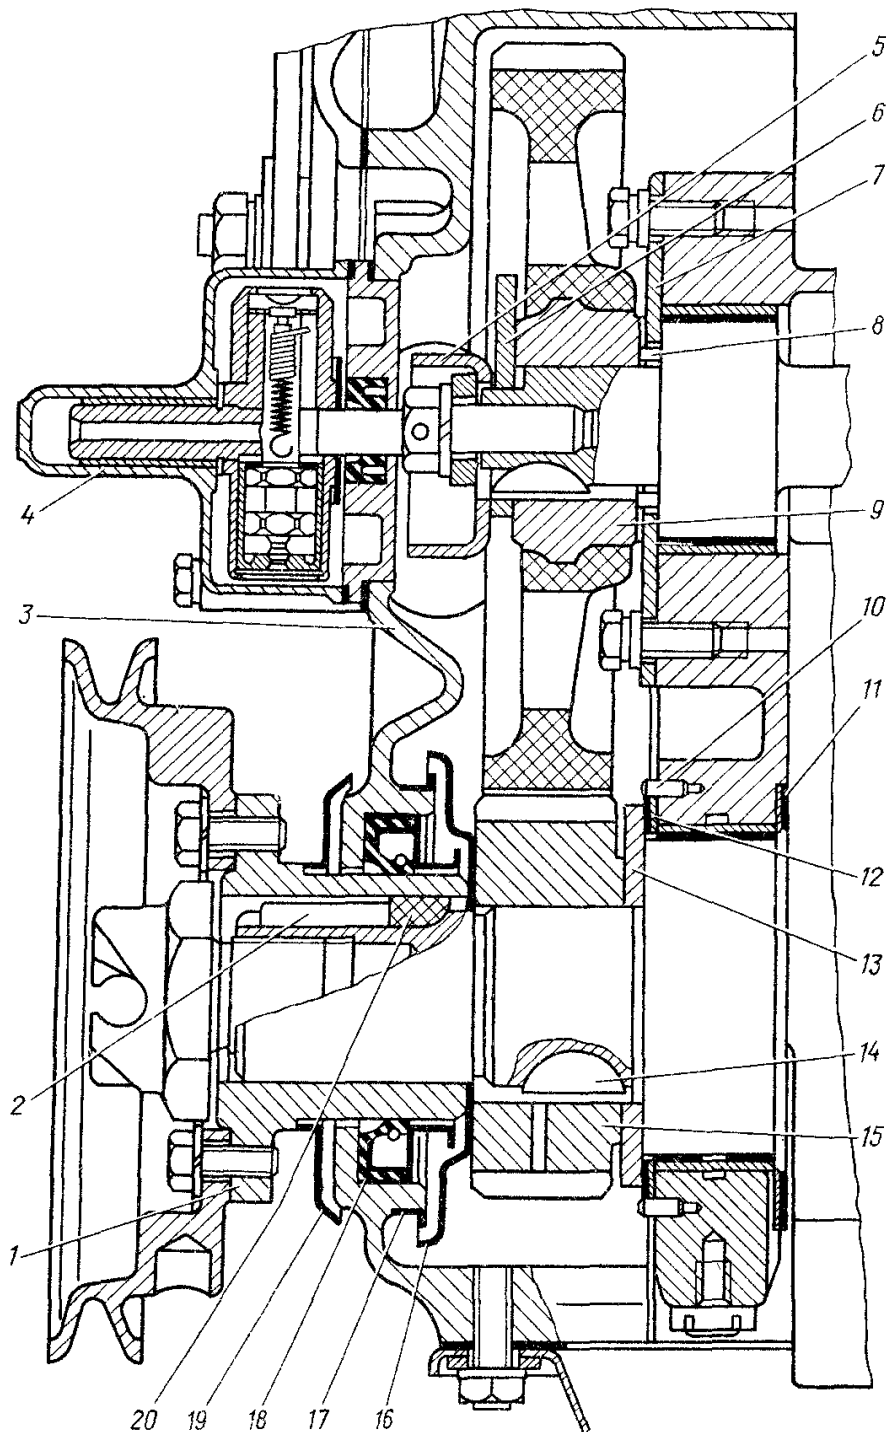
Передний конец коленчатого вала и привод распределительного вала:
